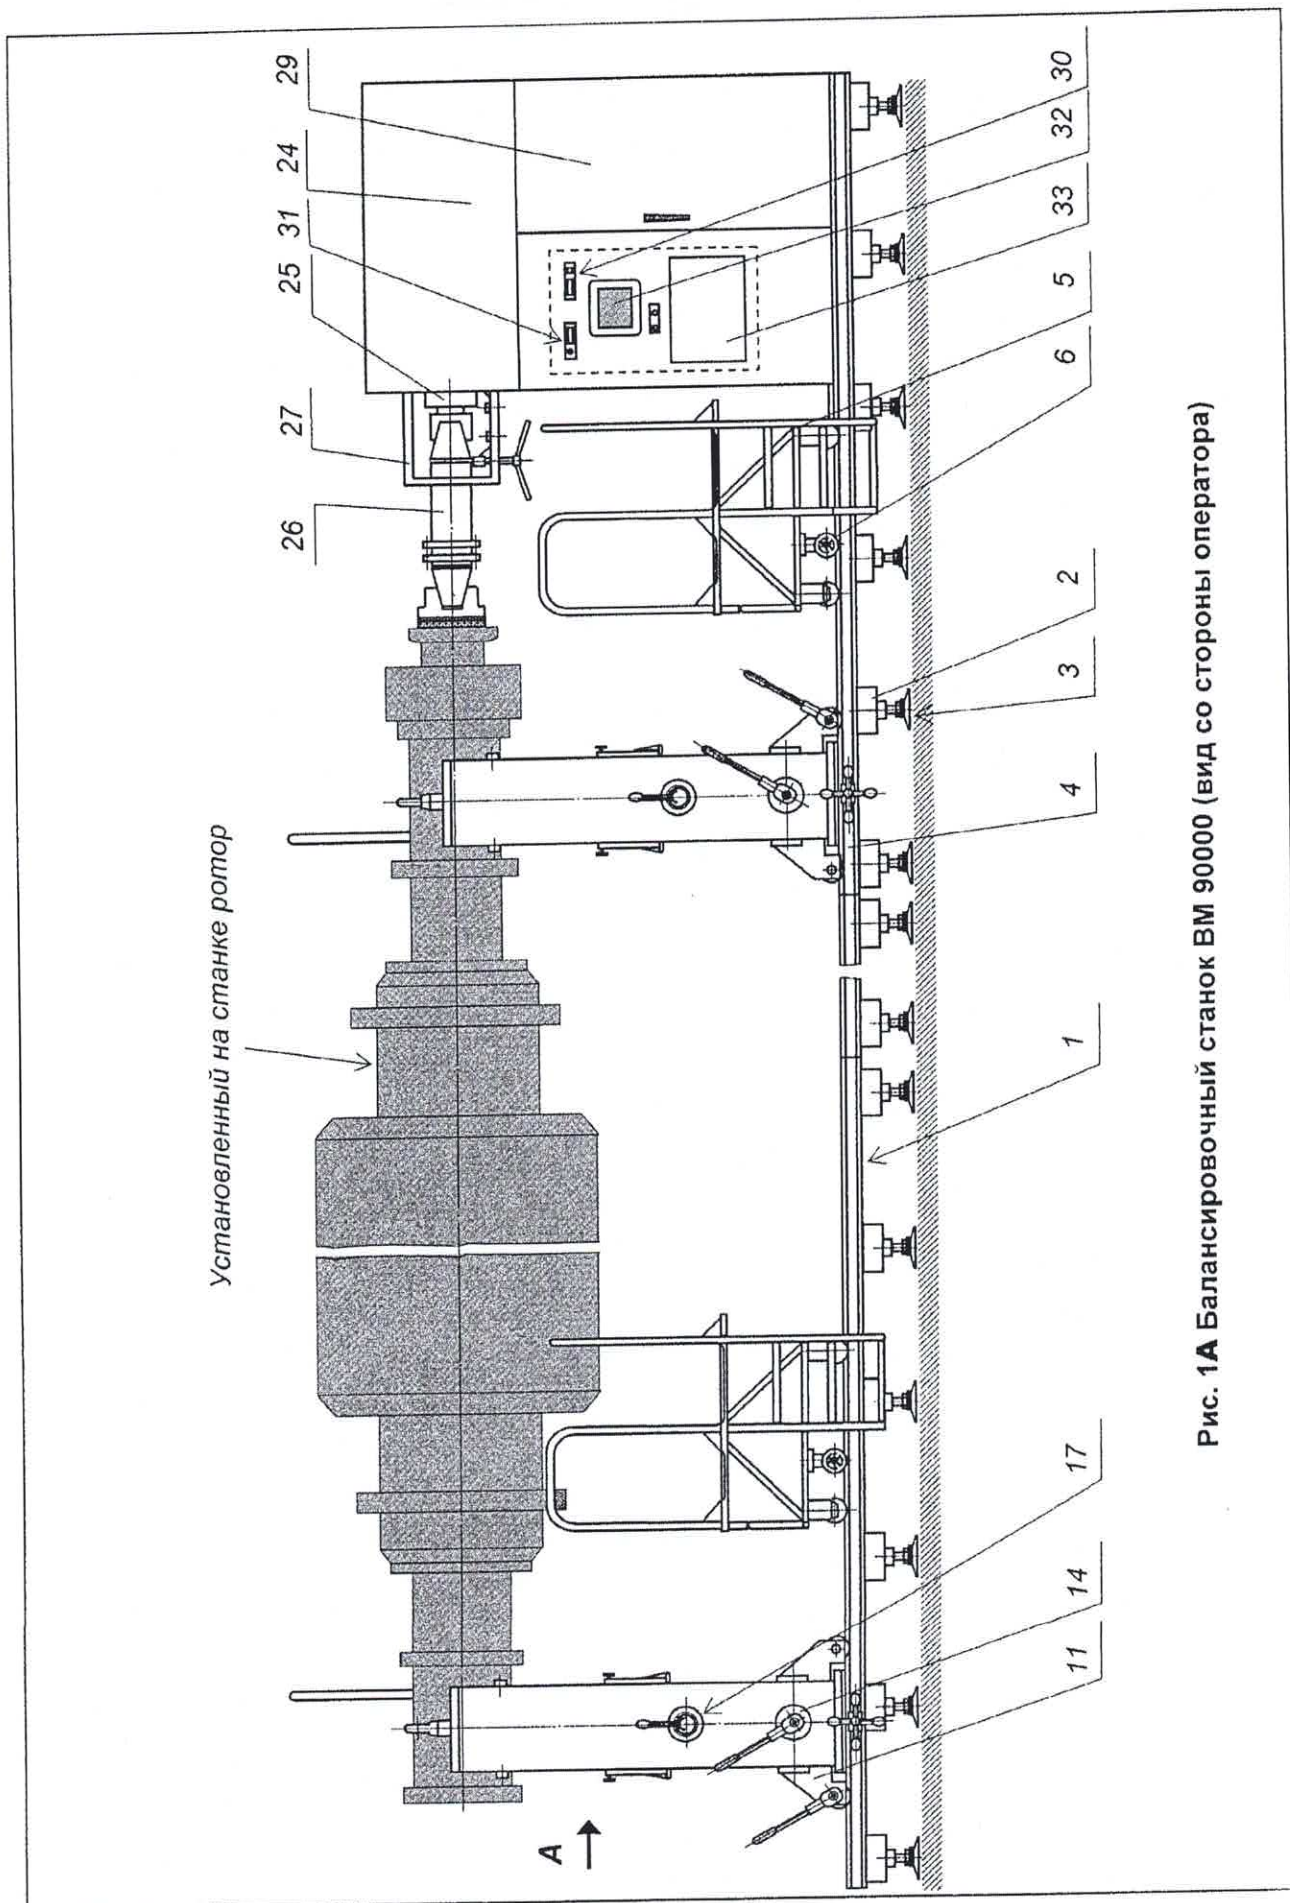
А Балансировочный станок BM 90000 (вид со стороны оператора)
